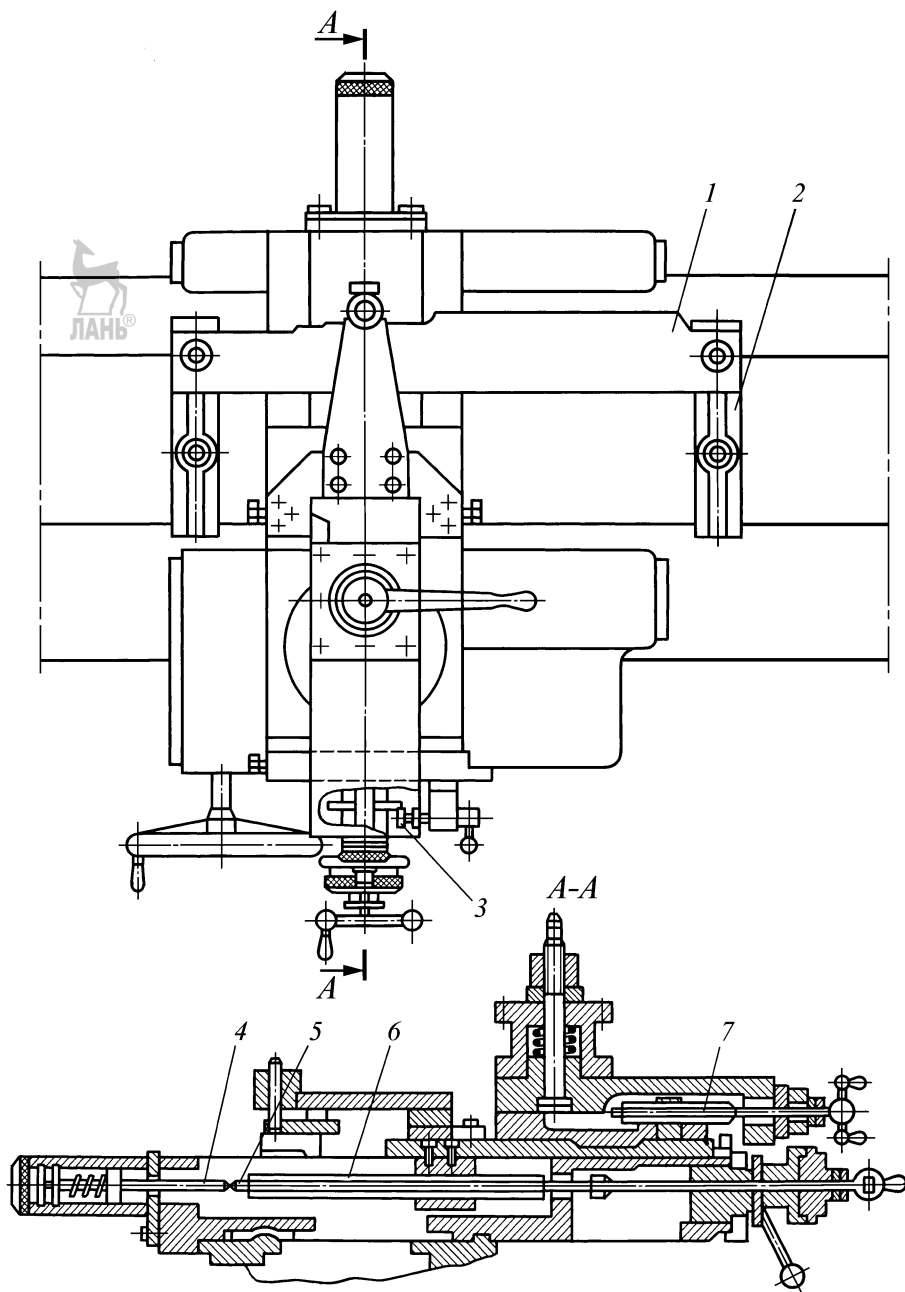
Копировальное устройство для обработки ступенчатых валов:
